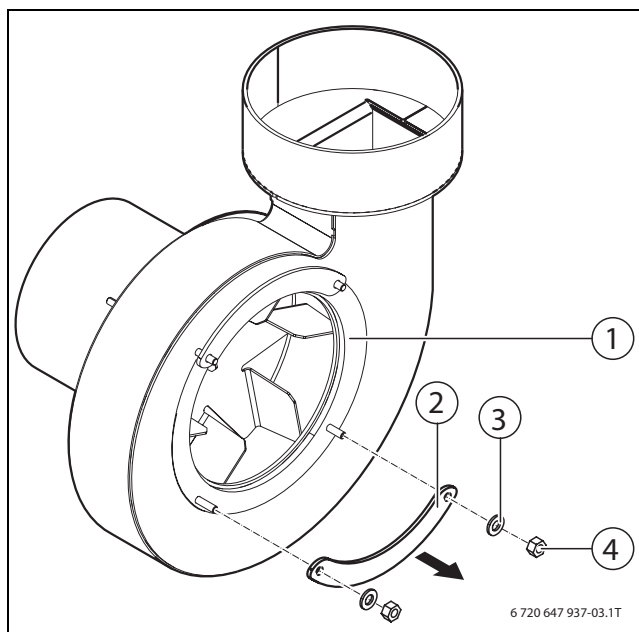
Smontaggio della staffa di fissaggio inferiore
